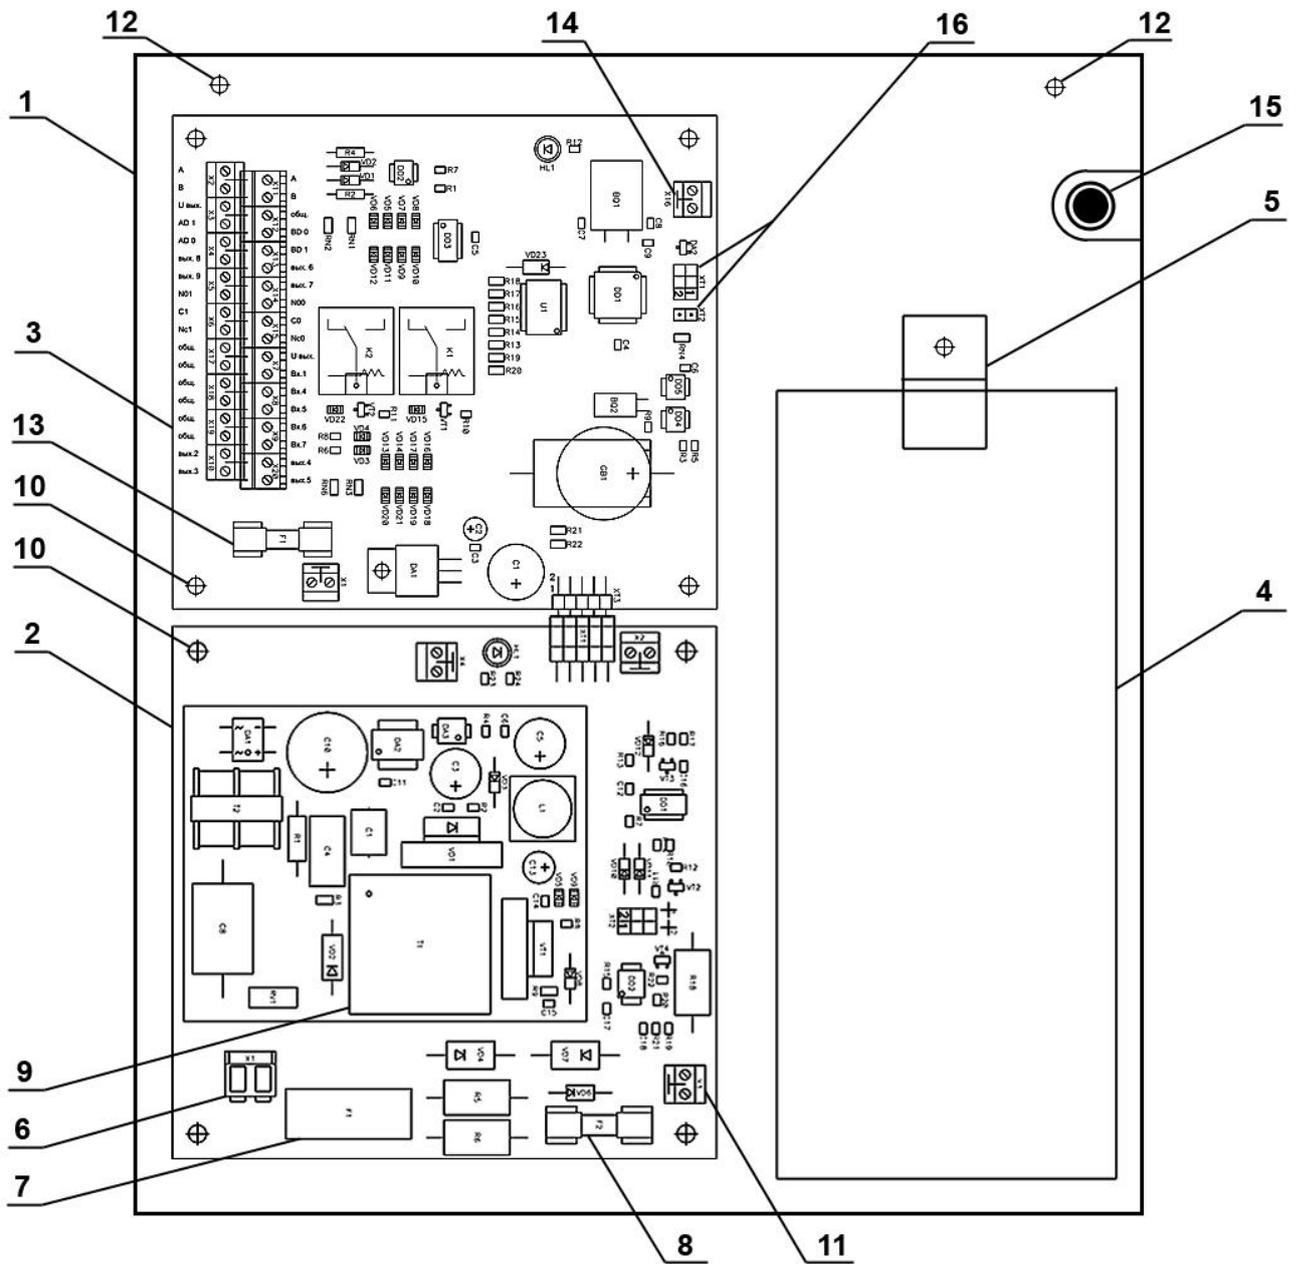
Внешний вид контроллера «Реверс К2»
